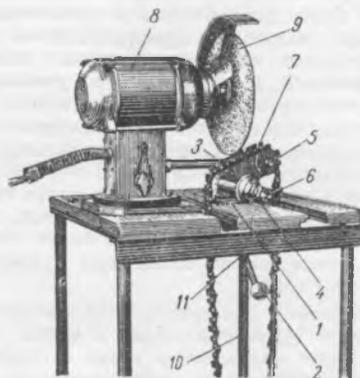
Приспособление к электроточилу для заточки пильных цепей: 1 — металлическая скоба; 2 — рукоятка механизма подъема держателя цепи; 3 — металлическая шина; 4 — рукоятка барабанчика для передвижения цепи; 5 — барабанчик для наклона держателя пильной цепи; 7 — пильная цепь; 8 — электроточило; 9 — точильный круг; 10 — пружинное натяжное приспособление для пильной цепи; 11 — металлическая втулка с резьбой для удержания натяжного приспособления.
